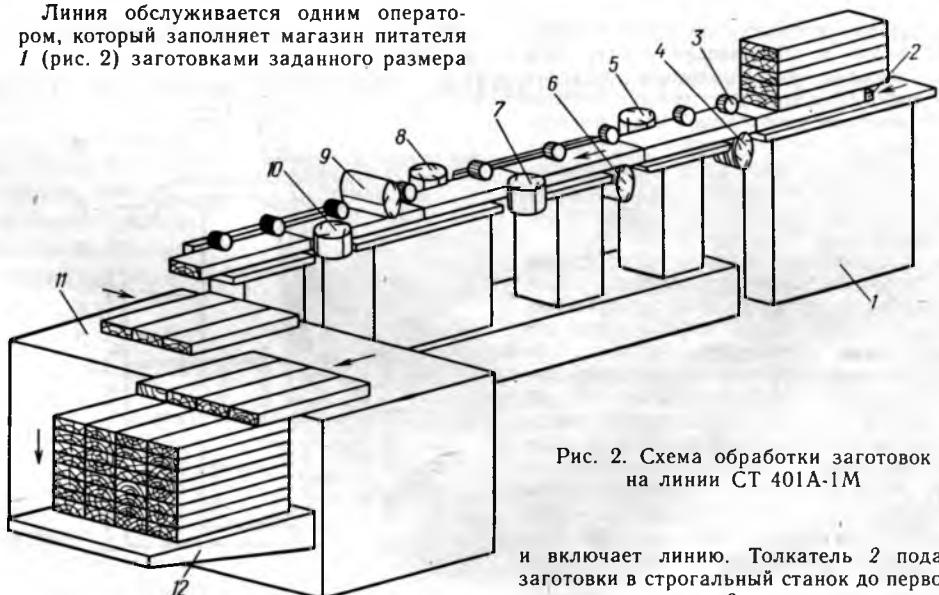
Схема обработки заготовок на линии СТ 401А-1М
